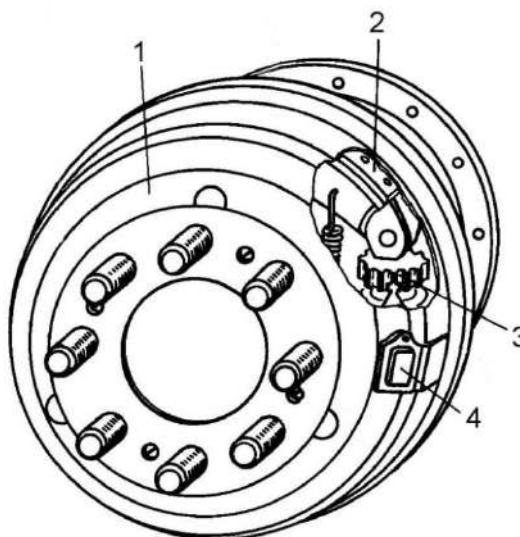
Регулировка механизма управления скоростью движения
